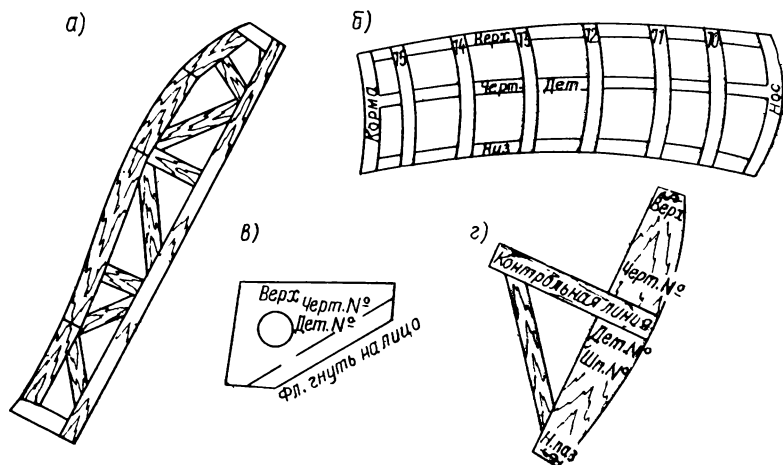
Шаблоны различного назначения: а — из досок для гибки шпангоута; б — из фанерных планок для контуровки листа наружной обшивки после гибки; в — фанерный (или дюралюминиевый) для разметки книц; г — из досок для проверки поперечной погиби листа наружной обшивки при гибке.
